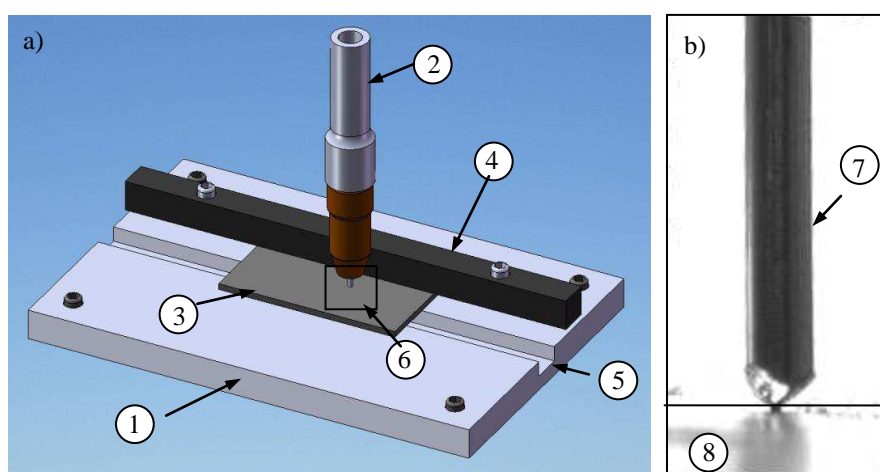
a) esquema de 1- Dispositivo de soldagem com 2- Tocha de soldagem, 3- Corpo de prova, 4- Viga de fixação, 5- Ranhura e 6- Área de foco da câmera , b) área de foco com 7- O arame e 8- A chapa (peça de trabalho)
